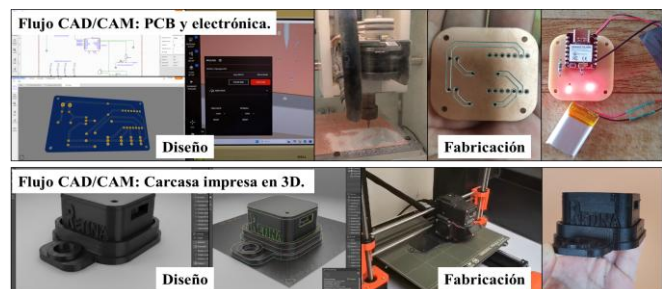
Flujo CAD/CAM de las PCB de prueba y carcasas.
